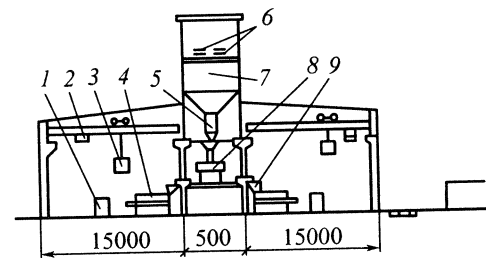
Схемы размещения смесительно-прессового оборудования:
